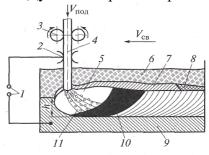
Схема дуговой сварки под флюсом: 1 – источник постоянного или переменного тока; 2 – скользящий контакт (токоподвод); 3 – подающий механизм; 4 – электродная проволока; 5 – парогазовый пузырь; 6 – флюс; 7 – расплавленный флюс; 8 – затвердевший шлак; 9 — свариваемый (основной) металл; 10 — сварочная ванна; 11 — сварочная дуга;  $V_{cb}$ ,  $V_{под}$  скорости сварки и подачи электродной проволоки; h - глубина проплавления основного металла
